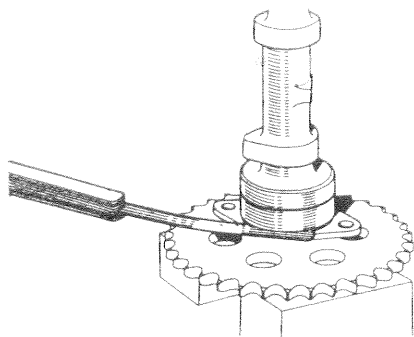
Arbre à cames - Contrôle du jeu à la bride
